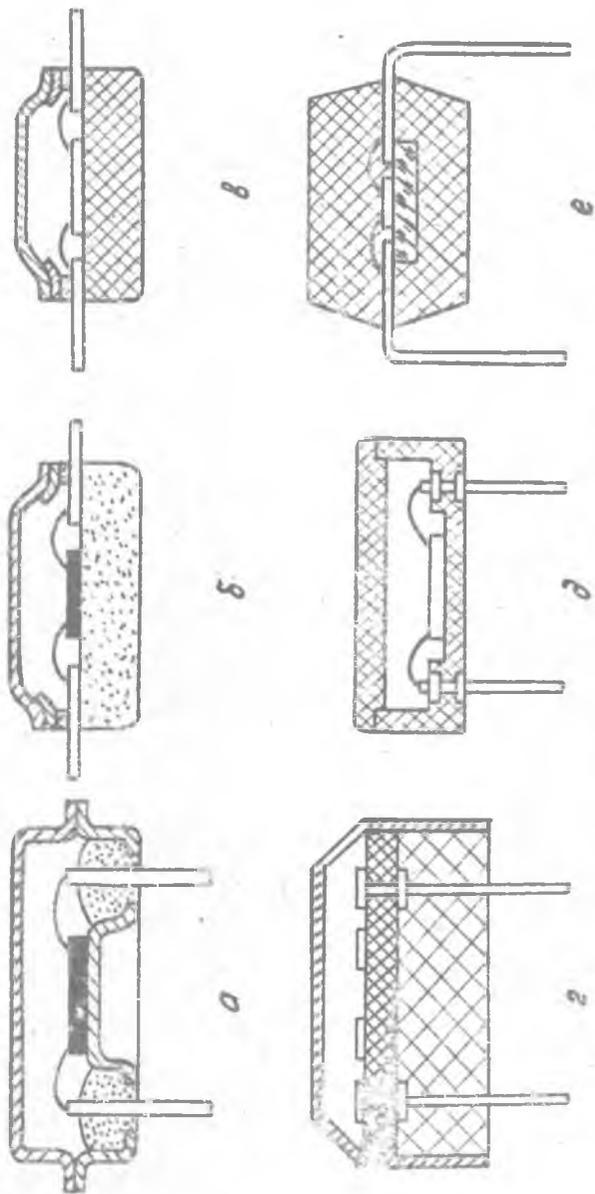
Конструкции корпусов: а - металлостеклянный, б - стеклянный, в - керамический, г - металлополимерный, д - пластмассовый, е - полимерный
